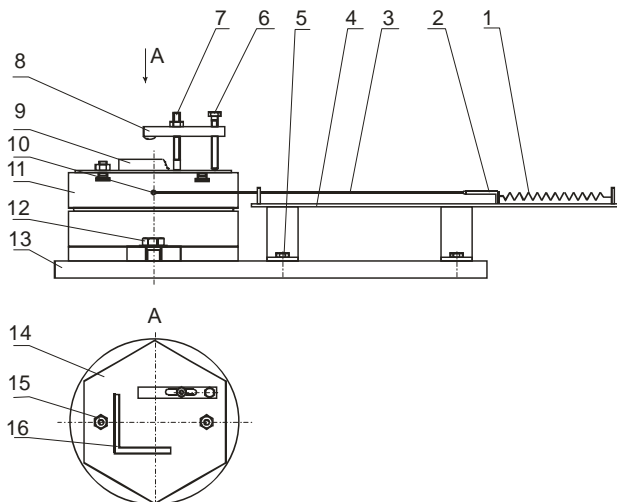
Экспериментальная установка: 1 – пружина; 2 – ползун; 3 – трос; 4 – планка; 5 – основание; 6 – болт; 7 – гайка; 8 – консоль; 9 – угол; 10 – болт; 11 – поворотный стол; 12 – болт; 13 – основание; 14 – пластина; 15 – болт.
